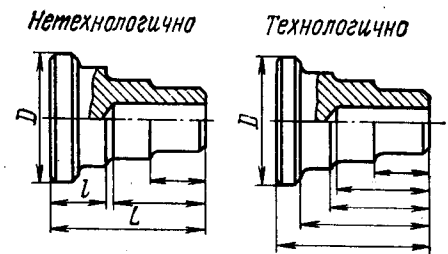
Простановка размеров на детали, предназначенной для обработки на револьверном станке.
